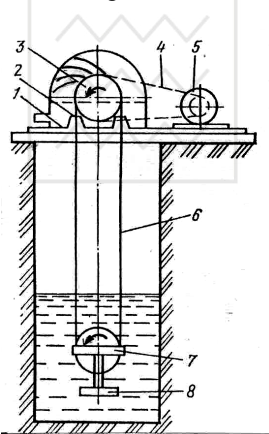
Схема установки стрічкового водопідійомника: 1- опірна рама; 2- корпус; 3,7- ведучий і нижній шків; 4- клинпасова передача; 5- двигун; 6- стрічка; 8- вантаж
